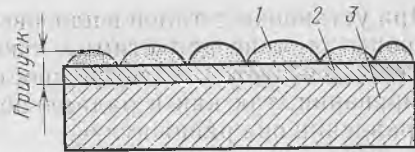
Схема разреза восстанавливаемой детали с образованным на ней припуском и дефектным слоем: 1 — дефектный слой; 2 — качественный слой; 3 — металл восстанавливаемой детали
